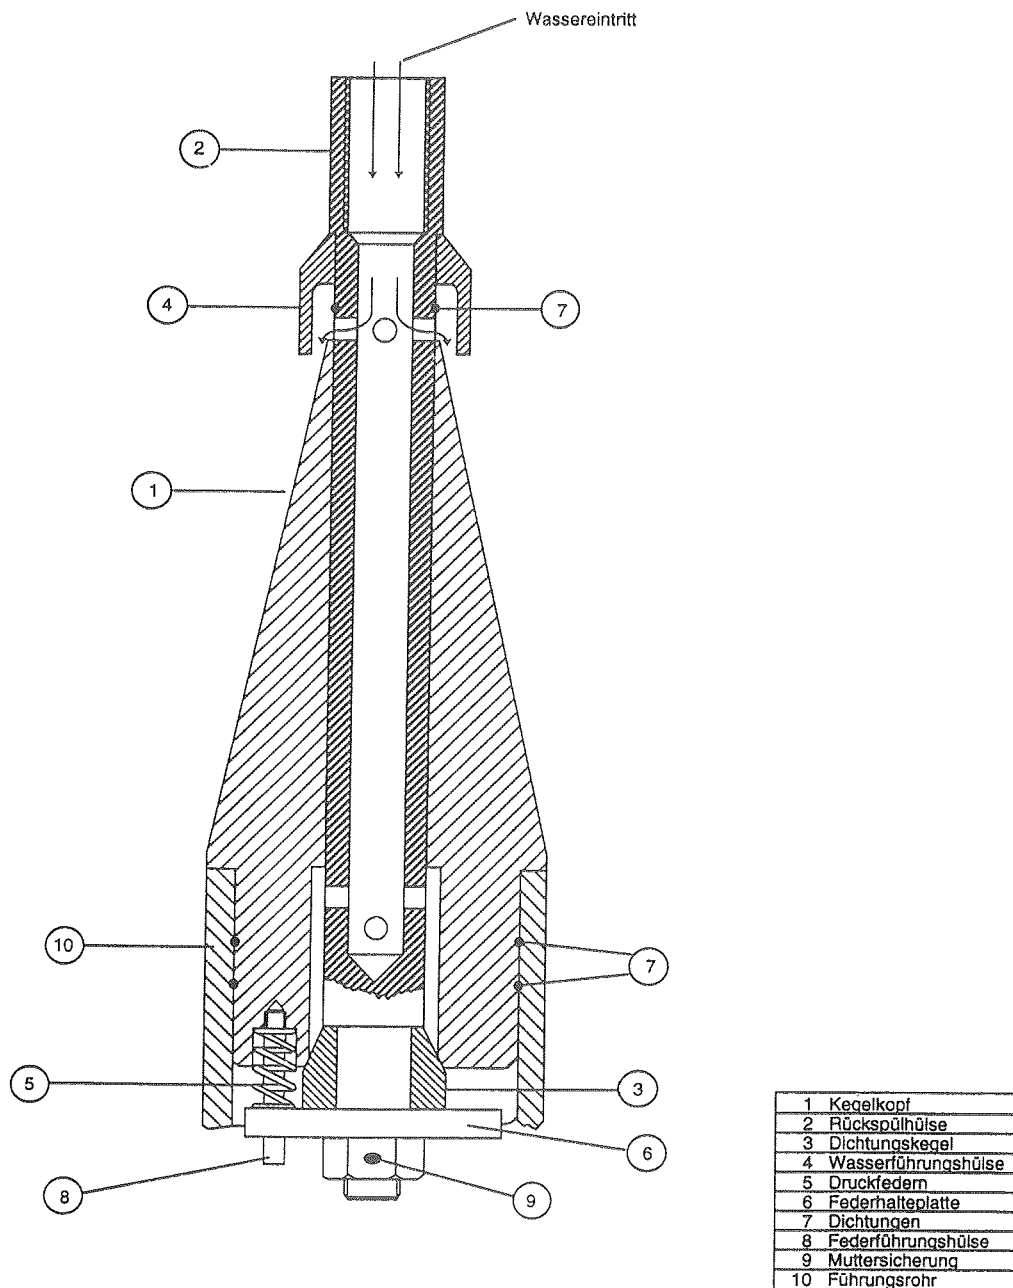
Oberes Ende der Bohrlanze mit 13 cm Durchmesser: Im Rückbohrbetrieb tritt das Wasser oben aus der Bohrlanze aus.
